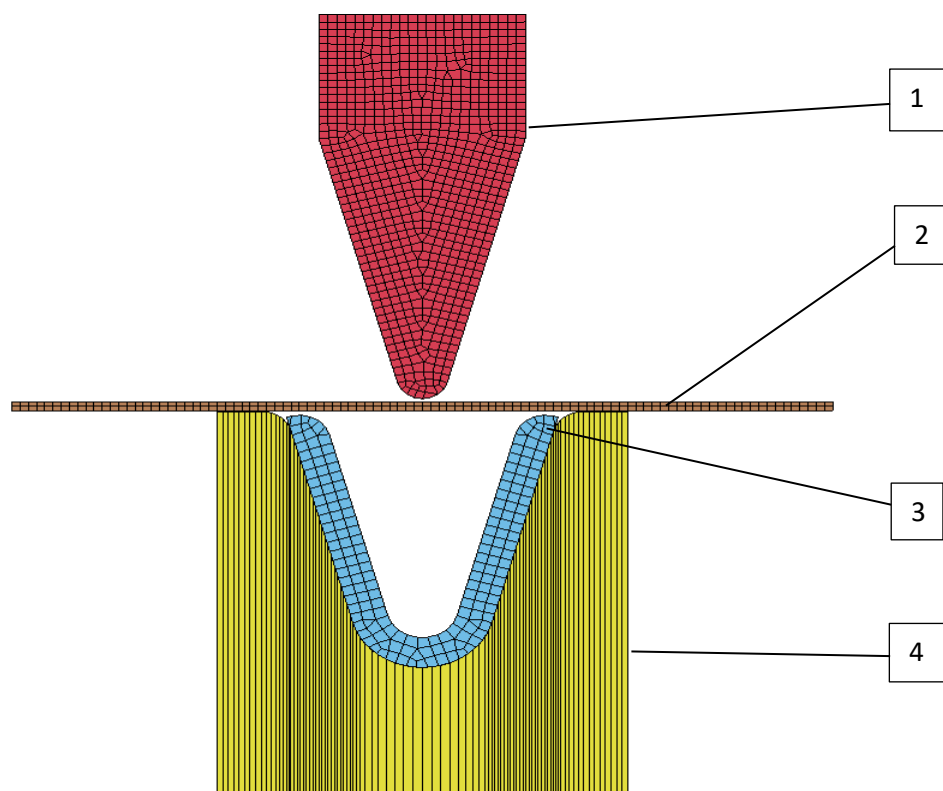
Сборка: 1- пуансон, 2- заготовка, 3- жёсткий элемент, 4- матрица
